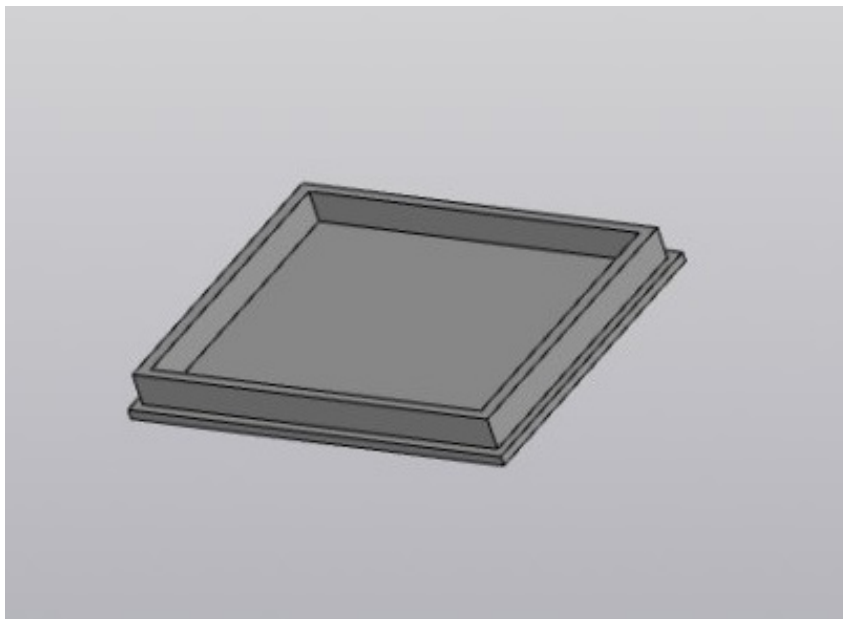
Задня частина корпусу пристрою, вигляд ззаду.
